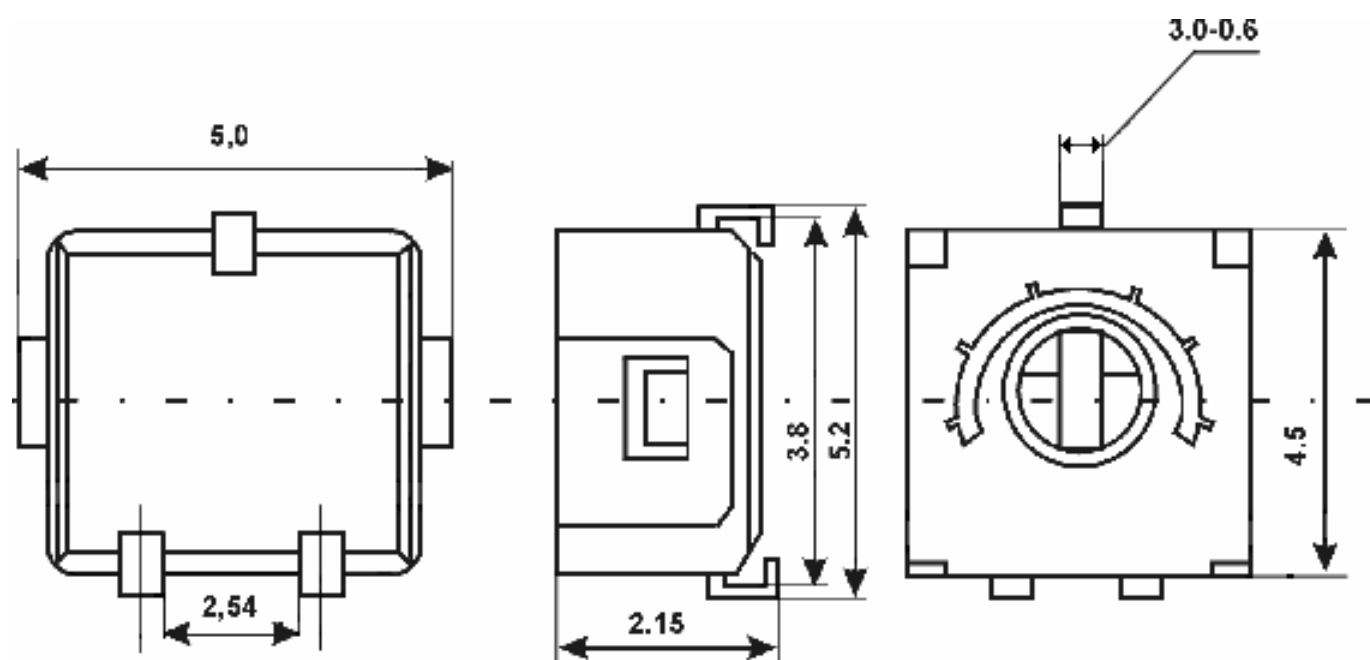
Конструкция, габаритные и присоединительные размеры корпусов ST-4A. Размер шлица - 3,2 (длина); 0,6 (ширина); 0,5 - глубина
